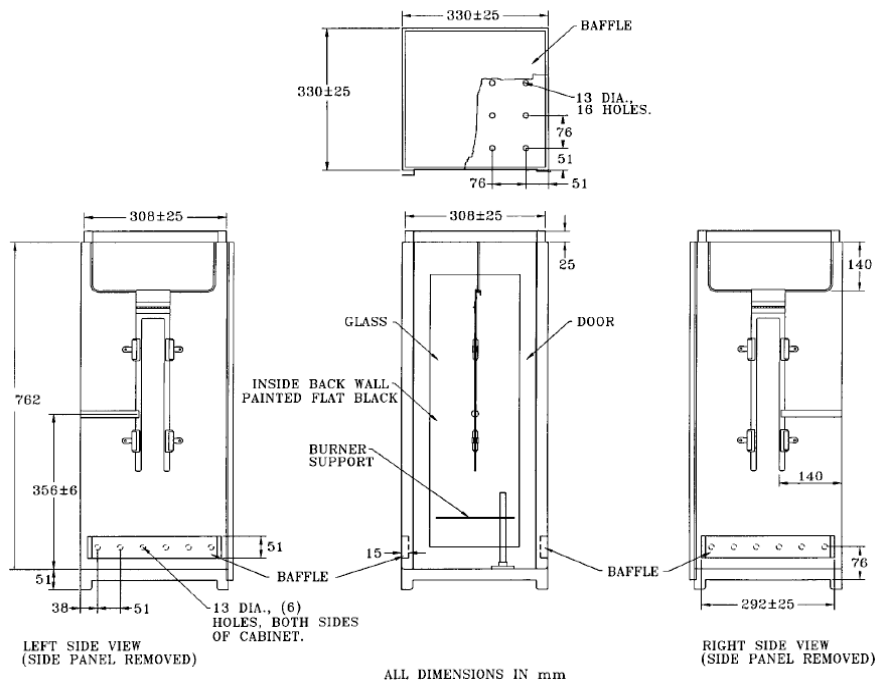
Detalles constructivos de la cámara de ensayos [4].
